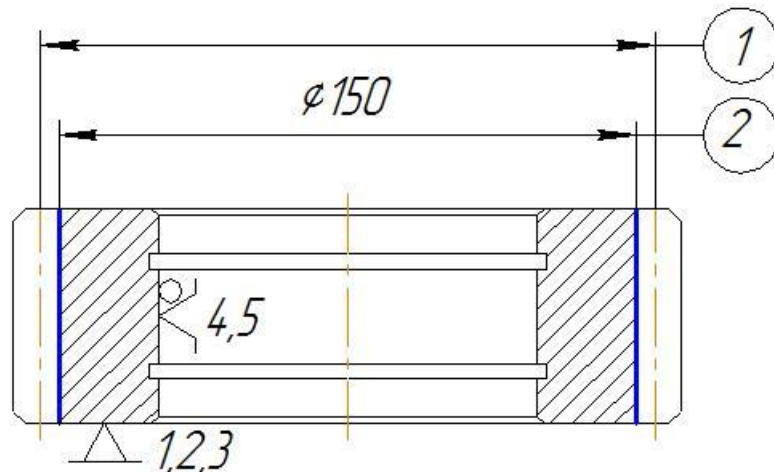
Схема базування заготовки при зубонарізанні
